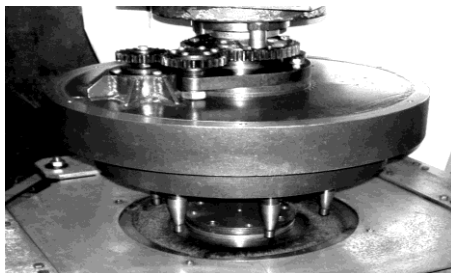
Шестишпindelный рабочий модуль установки типа кольцевая ванна с вертикальным расположением оправок з МНТП
